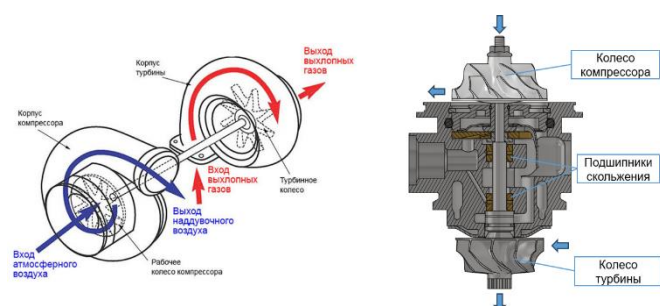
Принцип действия и устройство автомобильного турбокомпрессора
